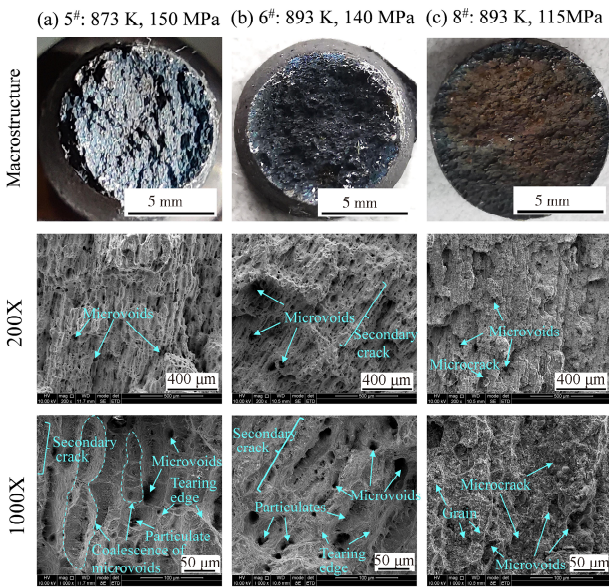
F92/Co3W2 焊接接头断口形貌
